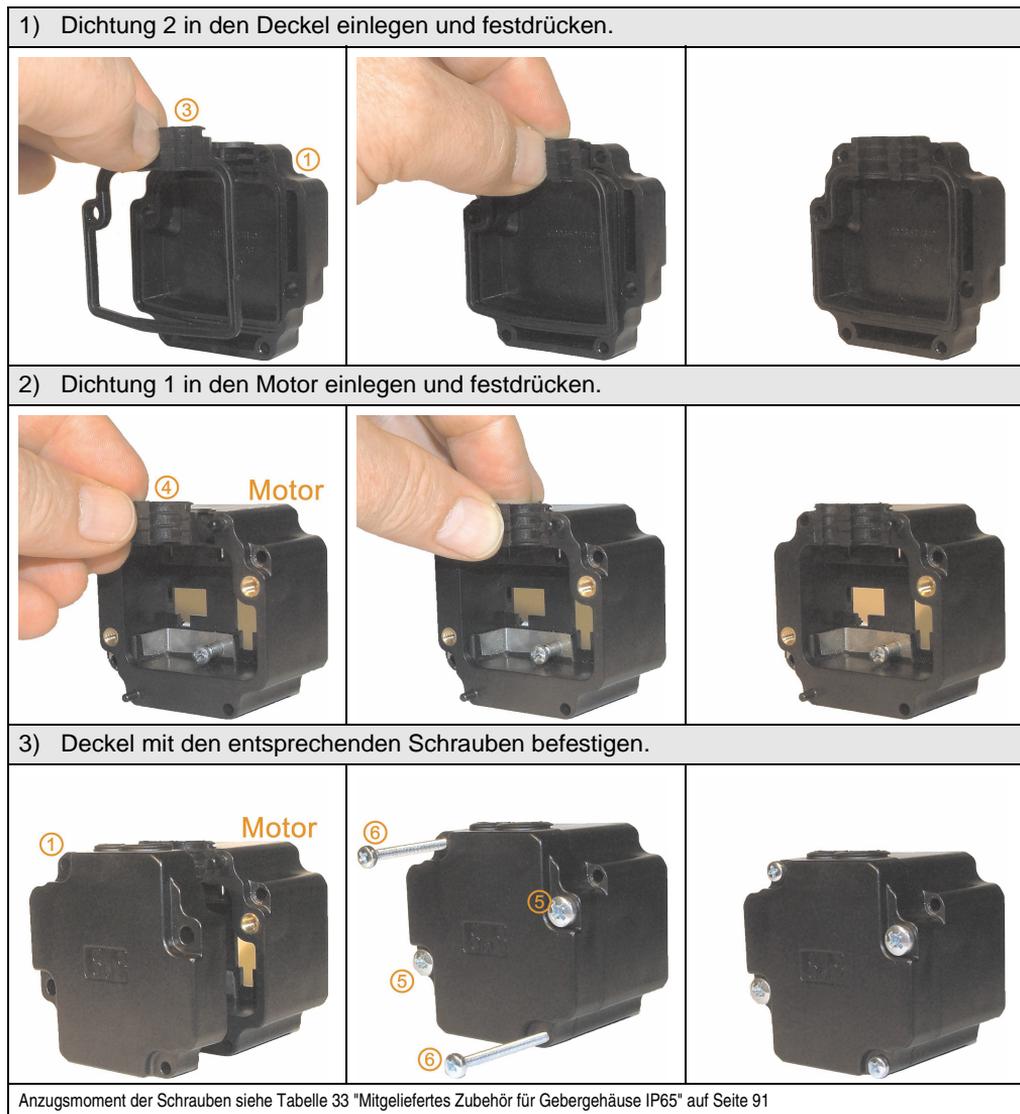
Montagehinweise - 80MPF-Motor, Deckel, Dichtungen, Schrauben
